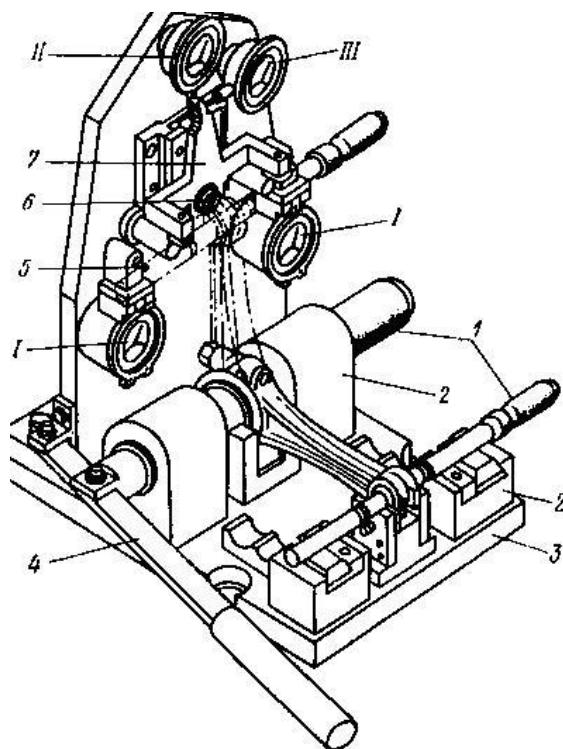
Приспособление для проверки и правки шатуна: 1 – скалки; 2 – стойки; 3 – плита; 4 – ручка; 5 – штифт; 6 – ось коромысла; 7 – коромысло; I, II, III – индикаторы.
